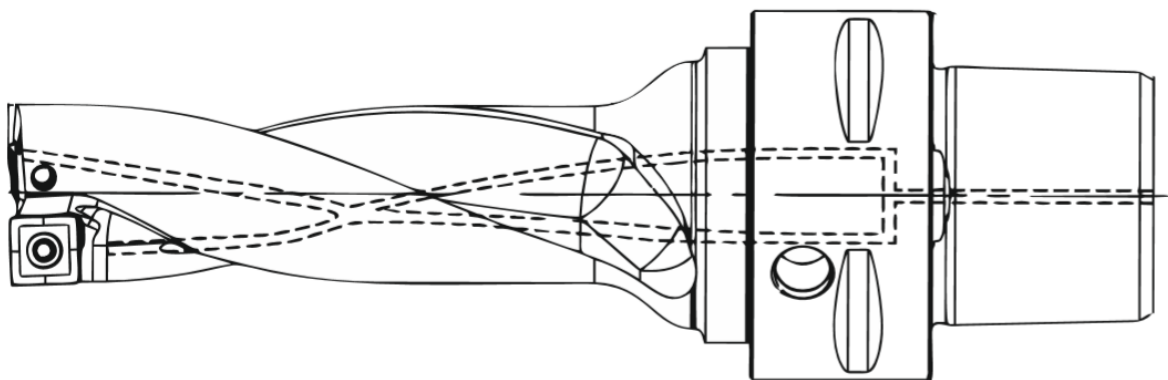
Свердло “CoroDrill 880” зі змінними пластинами
